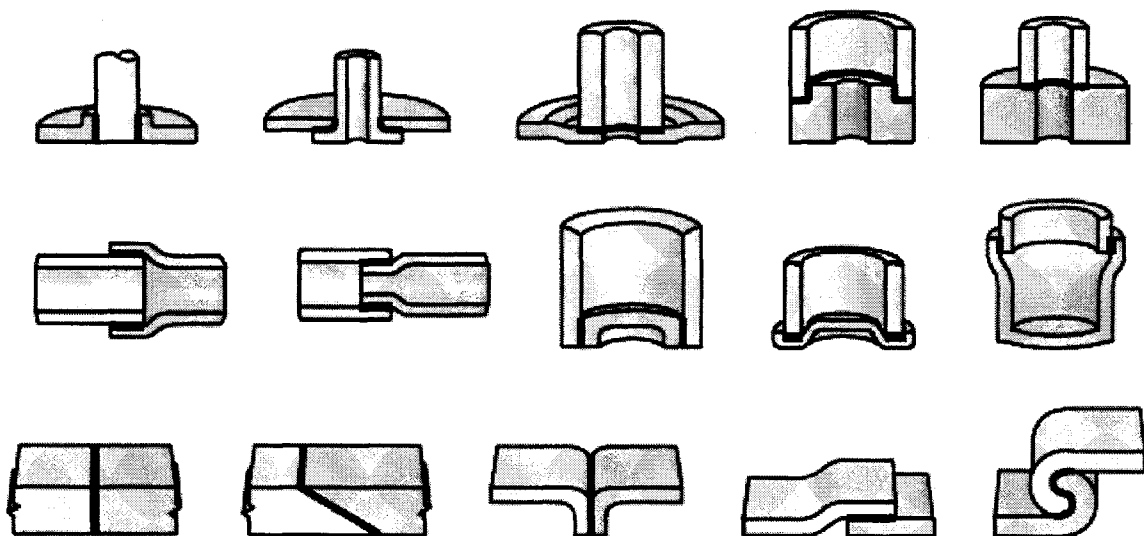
Diseño de uniones comúnmente usadas en los procesos de soldadura.
